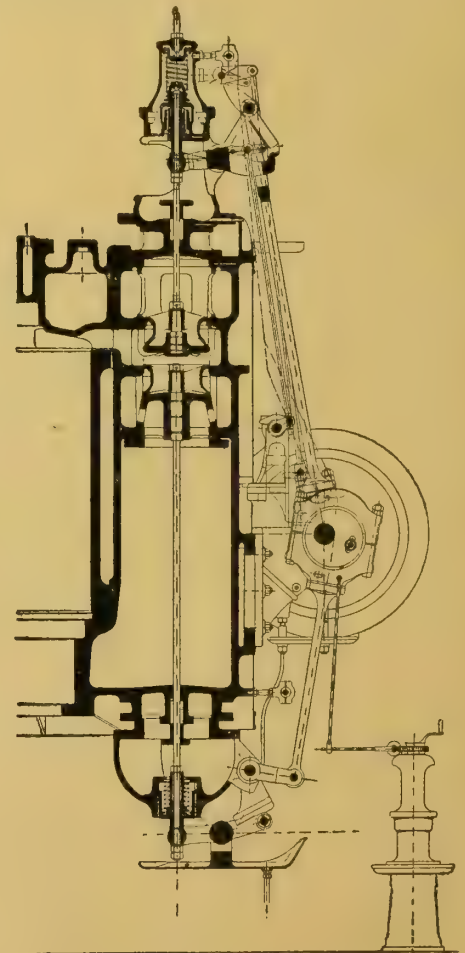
Steuerung des Hochdruckzylinders der Nürnberg-Augsburger Maschine.
